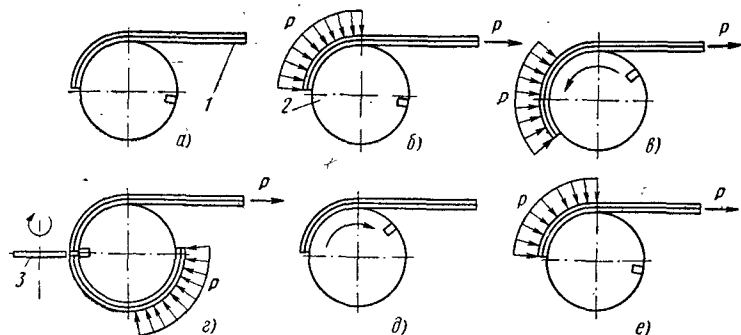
Схема штамповки полувкладышей из металлофторопластовой ленты
